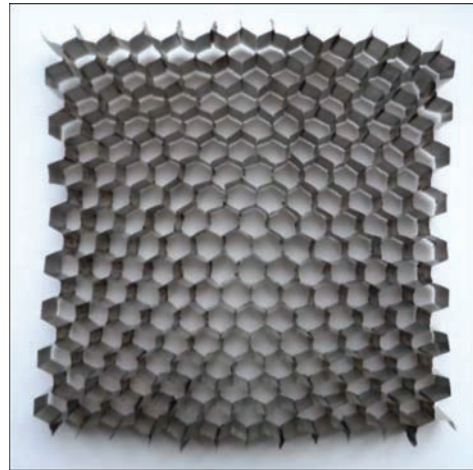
Сотовый заполнитель, изготовленный из фольги сплава ЮИПМ-1200
